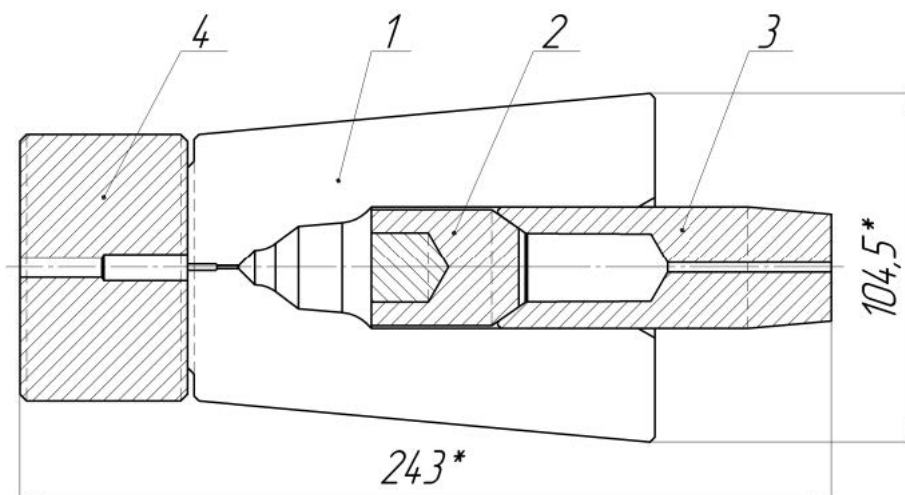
Внешний вид экспериментальной оснастки для изготовления резцов
